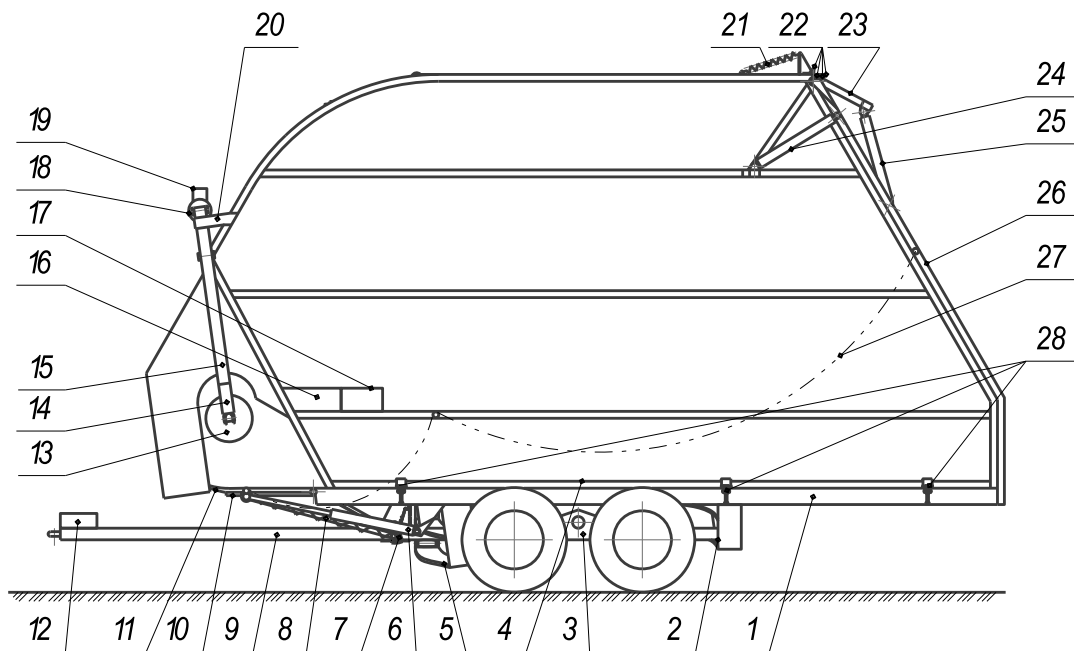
Транспортное средство для перевозки рулонов сена с самозагрузкой и саморазгрузкой, вид слева: 1 – платформа; 2, 5 – опорная дорожка; 3 – шасси; 4 – кузов; 6 – гидроцилиндры управления днищем; 7 – фиксатор прицепа; 8 – тяга; 9 – прицеп; 10 – рамка днища; 11 – днище; 12 – пульт управления; 13 – захват рулона; 14 – наставка; 15 – гидроцилиндр управления захватом; 16 – блок управления и сигнализации; 17 – гидрорас-пределитель; 18 – пневмоцилиндр; 19 – блок пневматических клапанов; 20 – зацеп; 21 – пружина; 22 – упор; 23 – выталкиватель; 24 – гидроцилиндр управления клапаном; 25 – гидроцилиндр управления выталкивателем; 26 – клапан; 27 – трос; 28 – зажим
